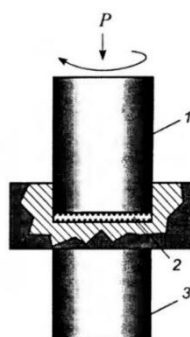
Схема ИПДК: 1 – пуансон; 2 – образец; 3 – суппорт [14]
